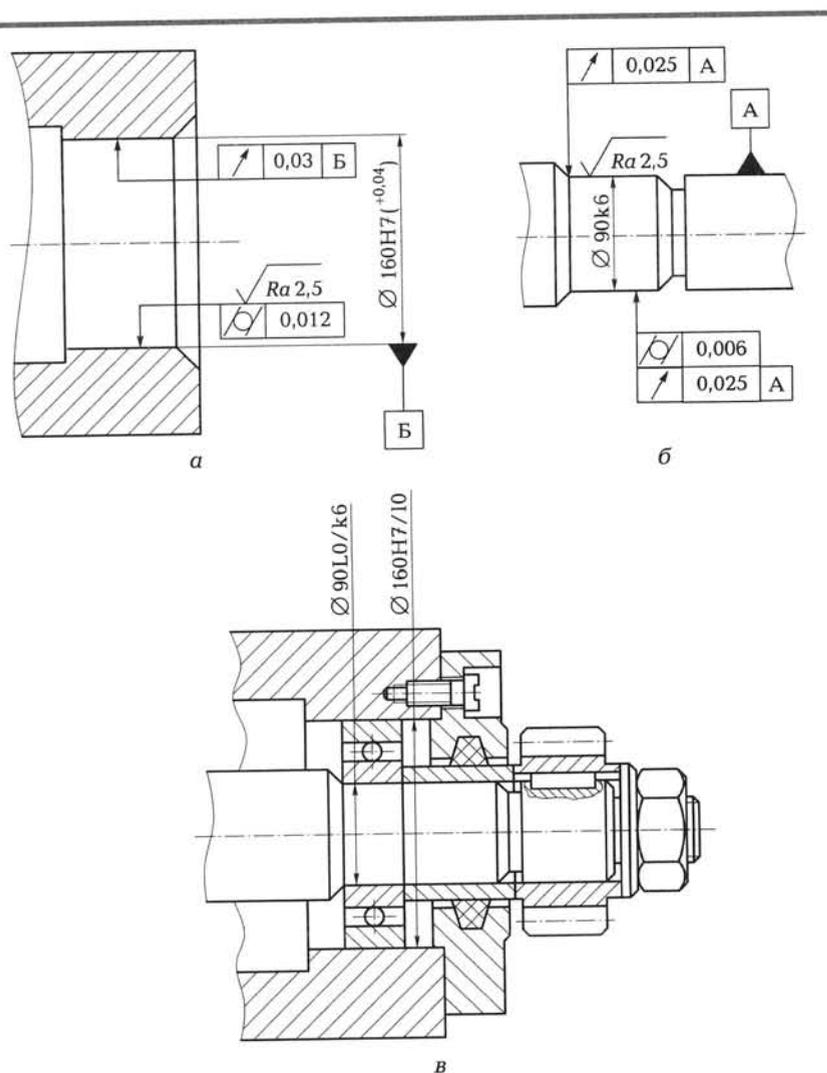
Обозначение полей допусков и посадок подшипников качения на чертежах:
